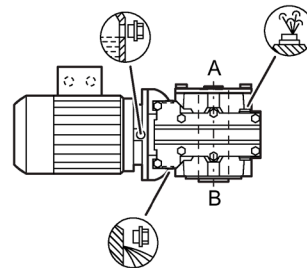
Einbaulagen für Stirradschneckengetriebe CAD Aufsteckausführung Baugröße 29
